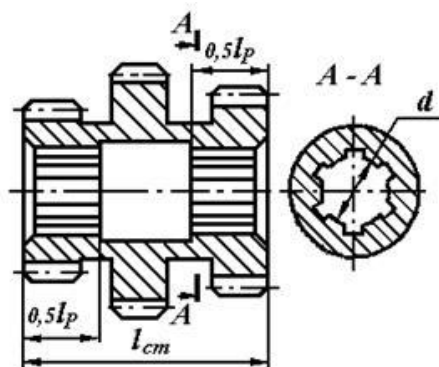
Шлицевое соединение блока шестерен с валом коробки передач
